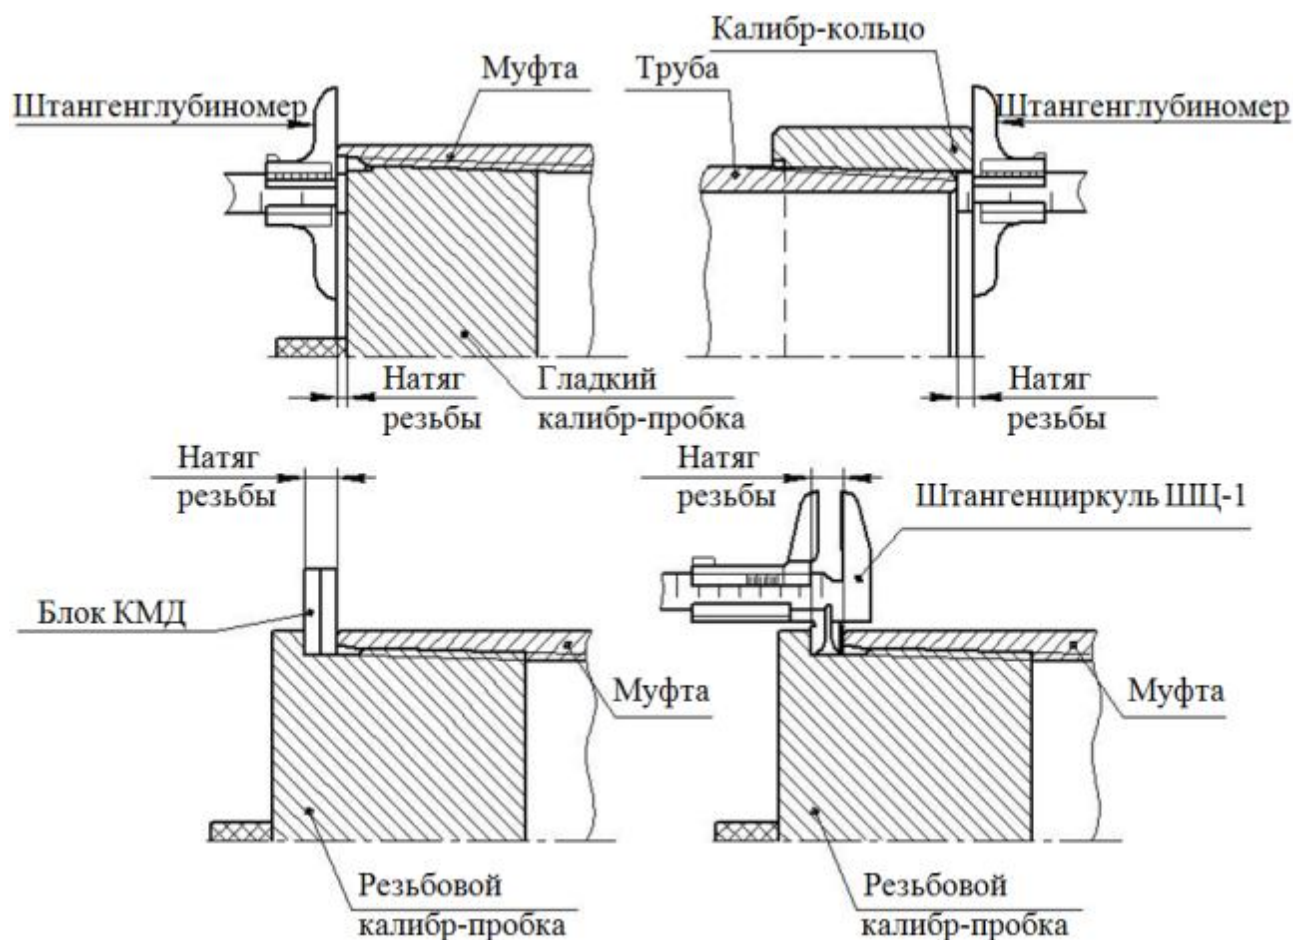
Схема измерения величины натяга резьбы трубы и муфты с треугольной и трапецеидальной резьбой
